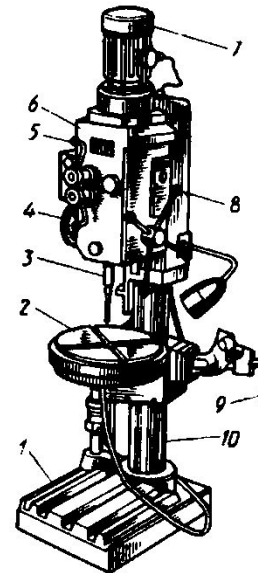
Универсальный вертикально-сверлильный станок 2Н125Л
